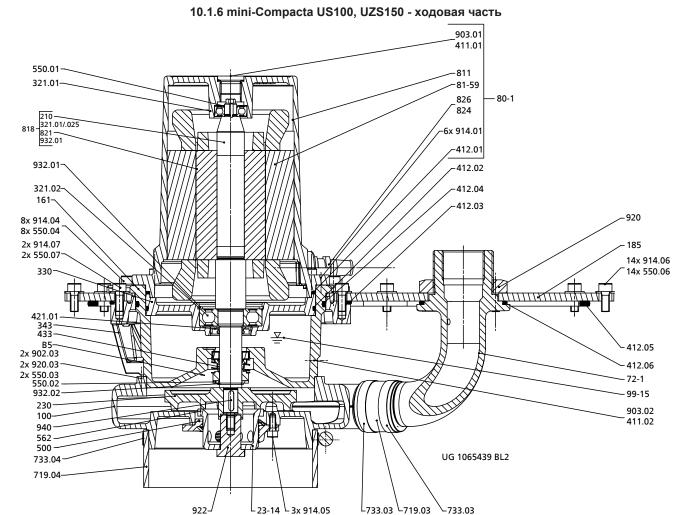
Обзорный чертеж US100, UZS150 - ходовая часть
